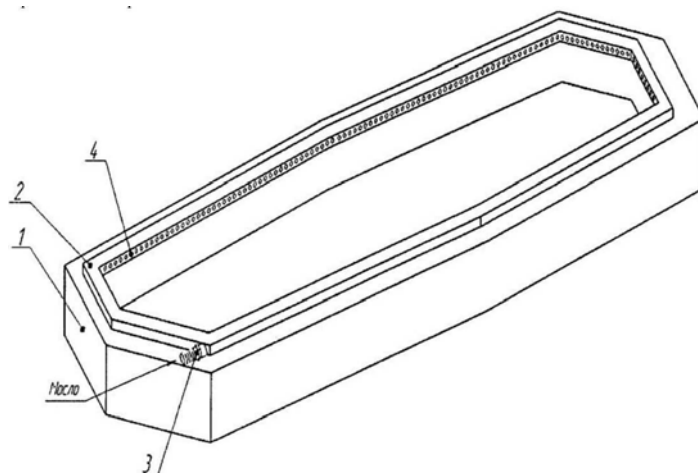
Общий вид кристаллизатора: 1 – корпус кристаллизатора; 2 – крышка кристаллизатора; 3 – впускной патрубок устройства подачи смазки; 4 – выходные отверстия [90, 104]
